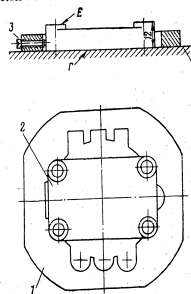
Кольцо для закрепления деталей из жаропрочных сплавов на столе плоскошлифовального станка.
